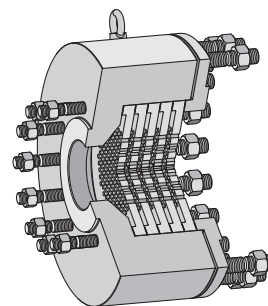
· Type 3381-3-5, vue en coupe 5 niveaux
